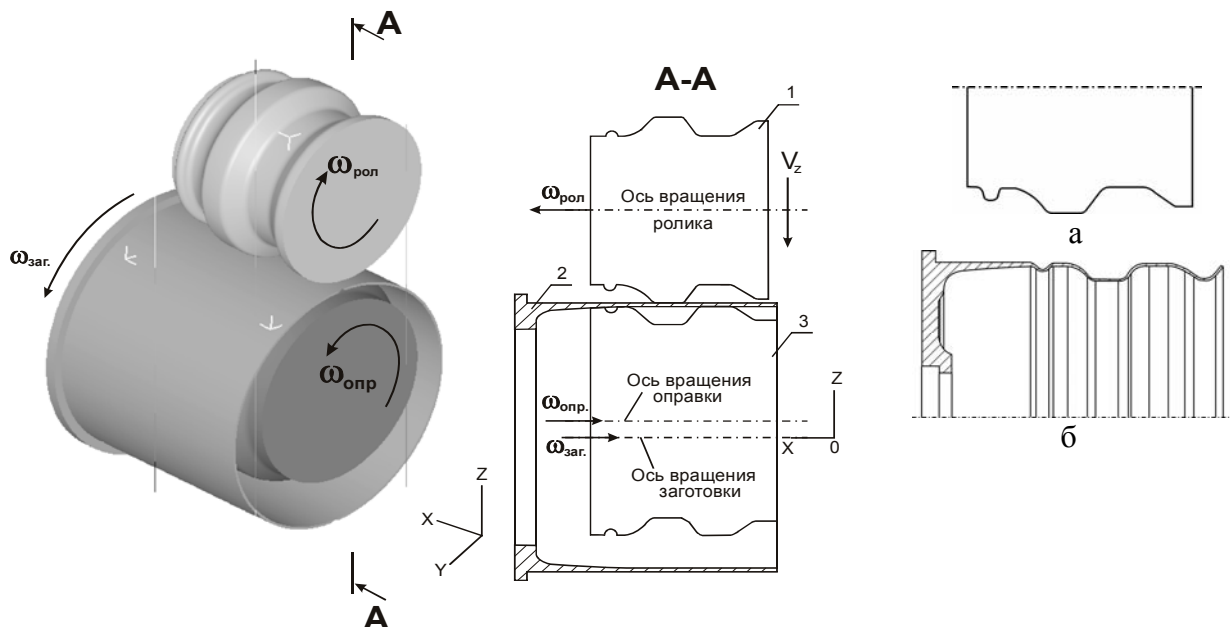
Схема процесса ротационной формовки с образованием рифтов на цилиндрической поверхности:
